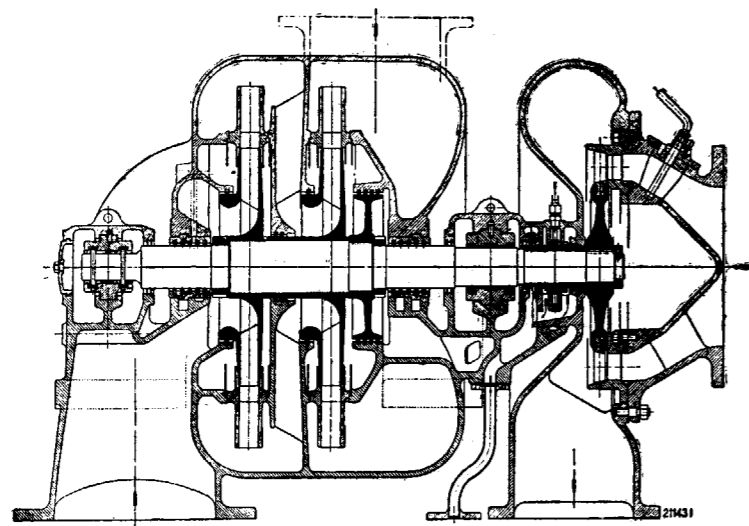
Soplante de sobrecarga con turbina de gas de escape para motor Diesel (método Büchi).
